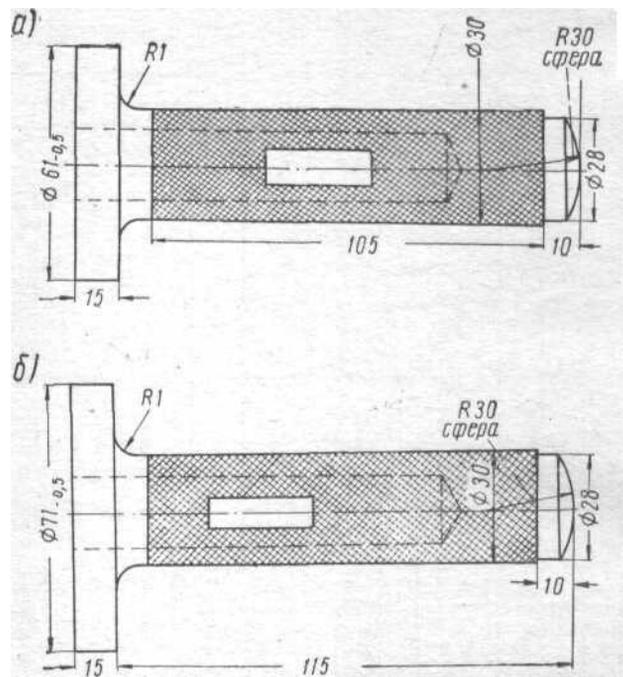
Оправки для запрессовывания наружных колец подшипников вала ведущей шестерни главной передачи:
